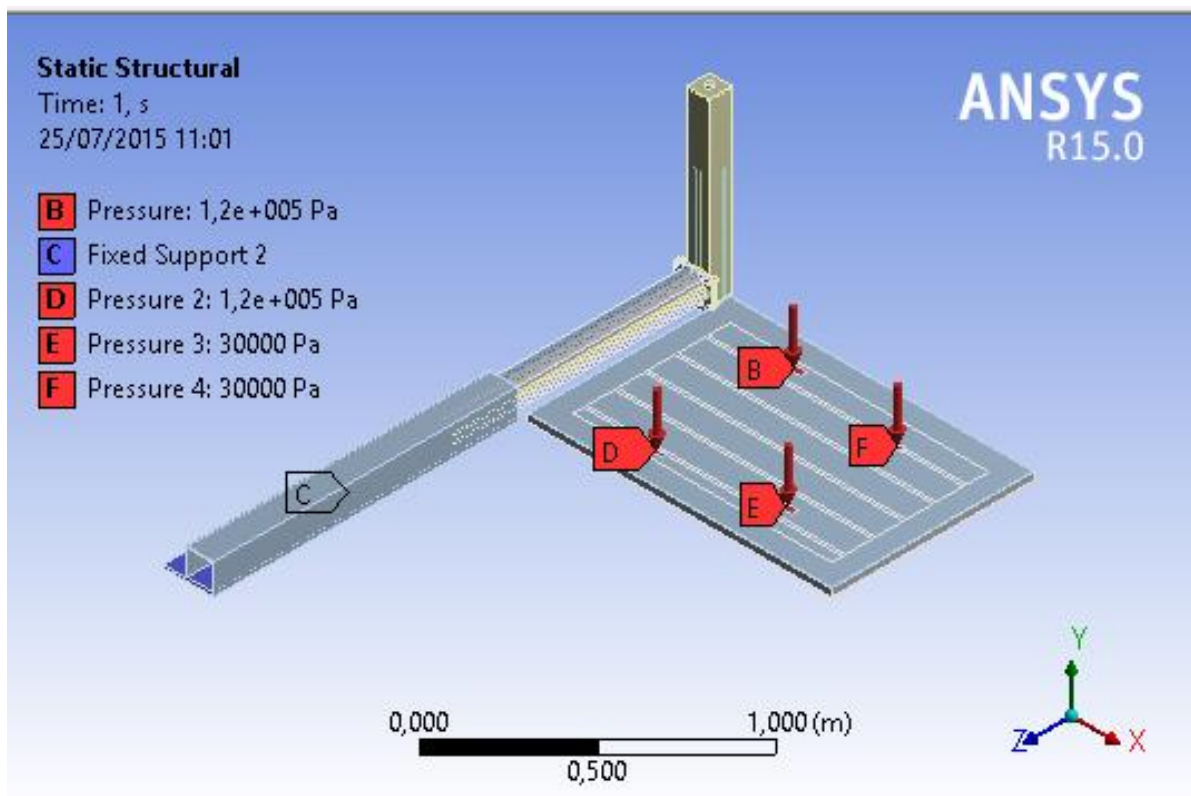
Aplicação de Cargas na Análise Estrutural - Plataforma Fechada
